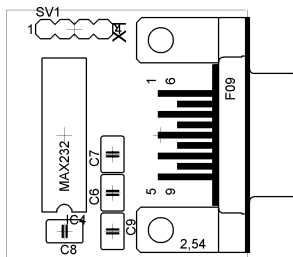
Deska plošných spojů převodníku ze strany součástek
